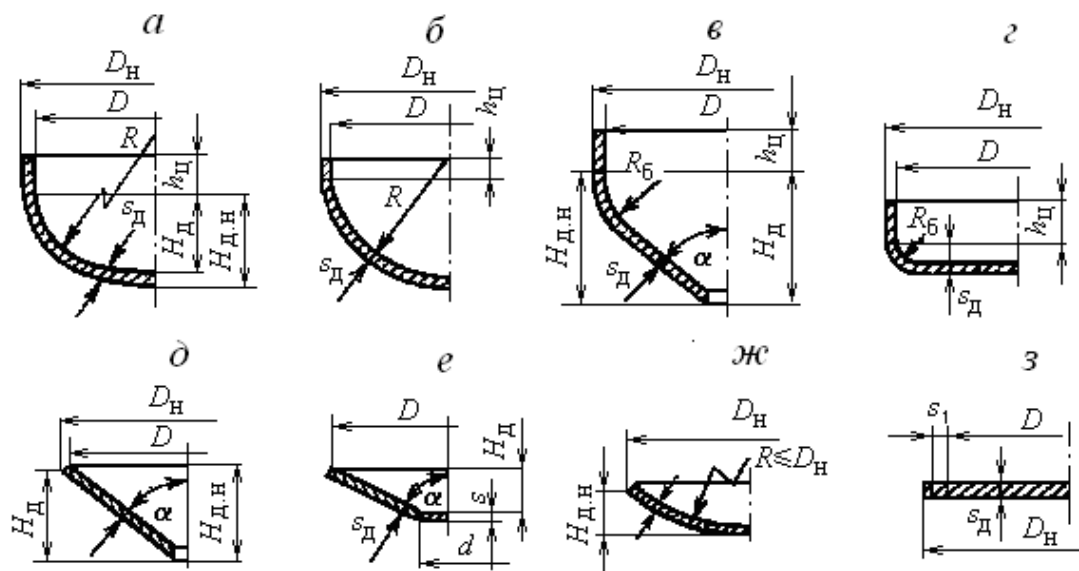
Основные конструкции днищ сварных аппаратов:
